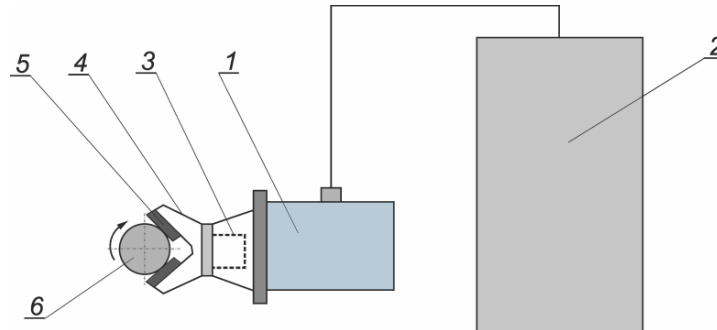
Схема установки для механо-ультразвукової оброблення:
